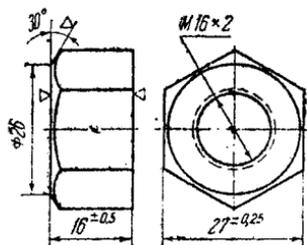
Дет. № 3037. Гайка к шпилькам крепления прижимной планки
